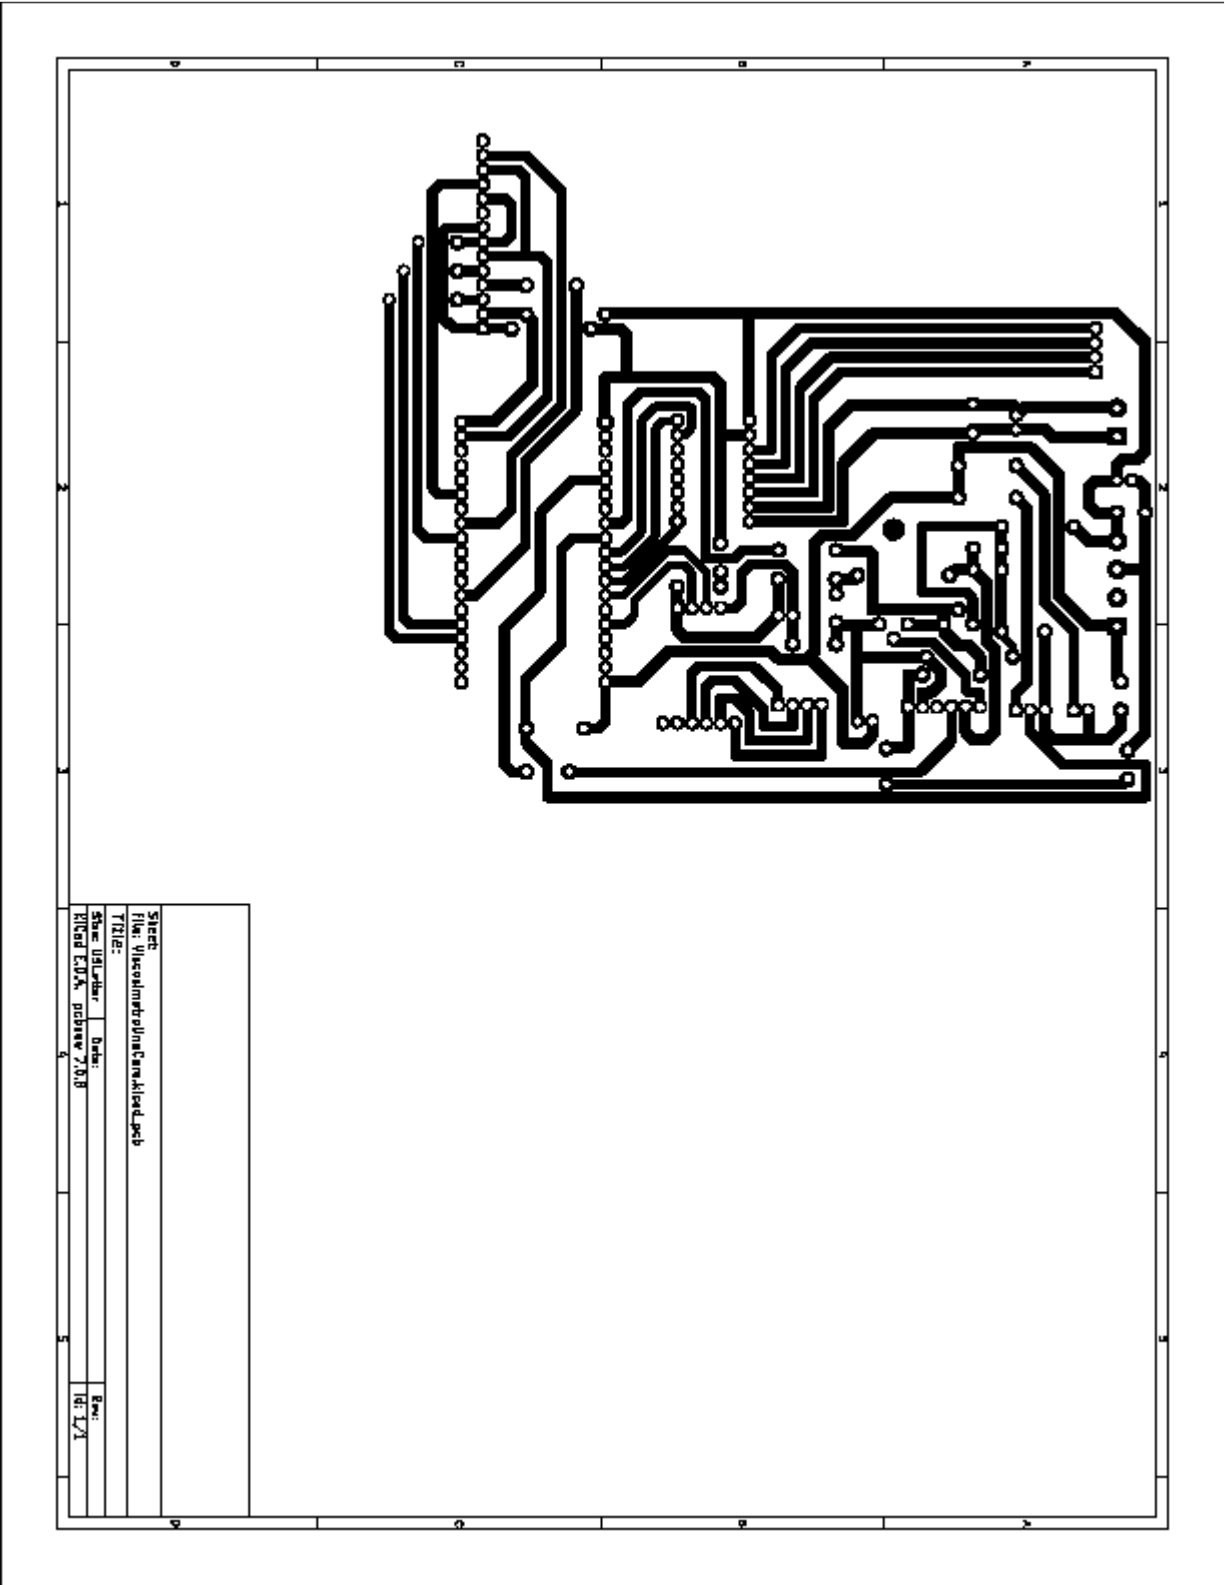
Circuito impreso, soldadura (Elaboración propia).
